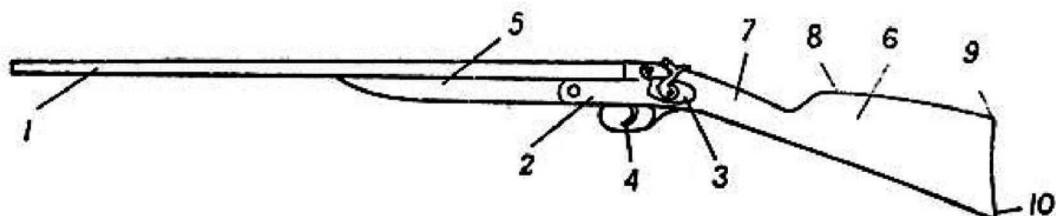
Общий вид ружья и его части: 1 - ствол; 2 - колодка; 3 - замок; 4 - спуск; 5 - цевье; 6 - приклад; 7 - шейка; 8 - гребень; 9 - пятка; 10 – носок
